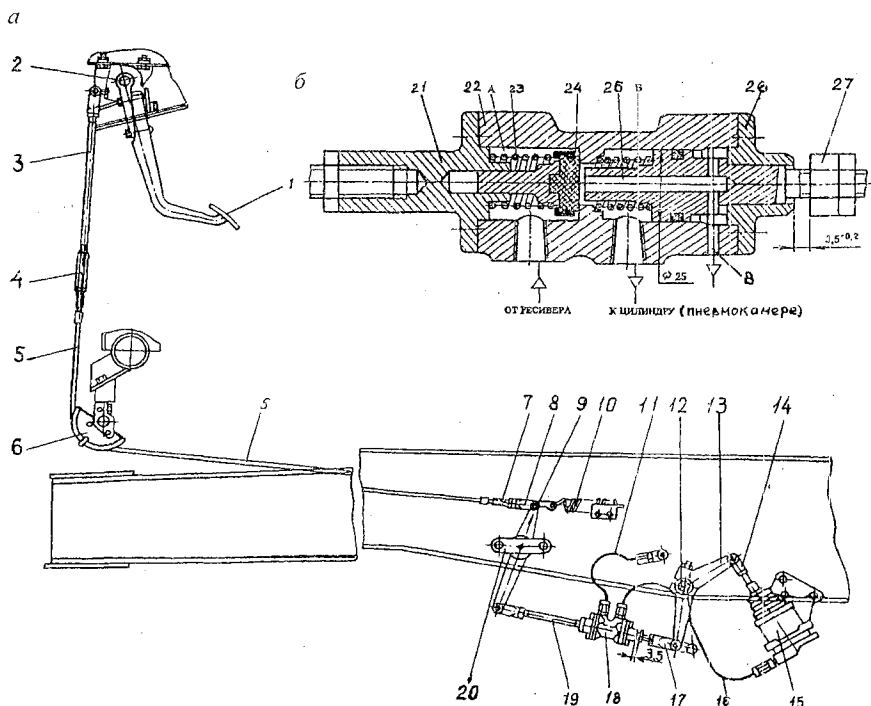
Механический привод выключения сцепления с пневмоусилителем:
